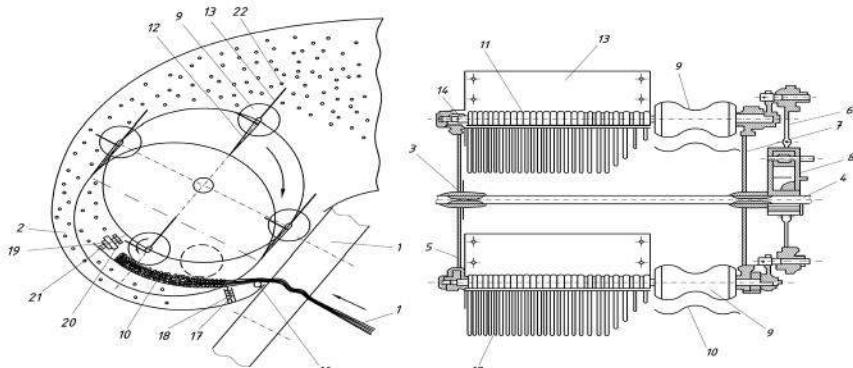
Плющильно-обчисувальний апарат: 1 – затискний транспортер; 2 – камера очосу; 3 – барабан; 4 – вал; 5, 6, 7, 8 – диски; 9 – криволінійні плющильні вальці; 10 – криволінійна опорна направляюча поверхня; 11 – гребені; 12 – зубці; 13 – пластини; 14 – вісь; 15 – стебла
